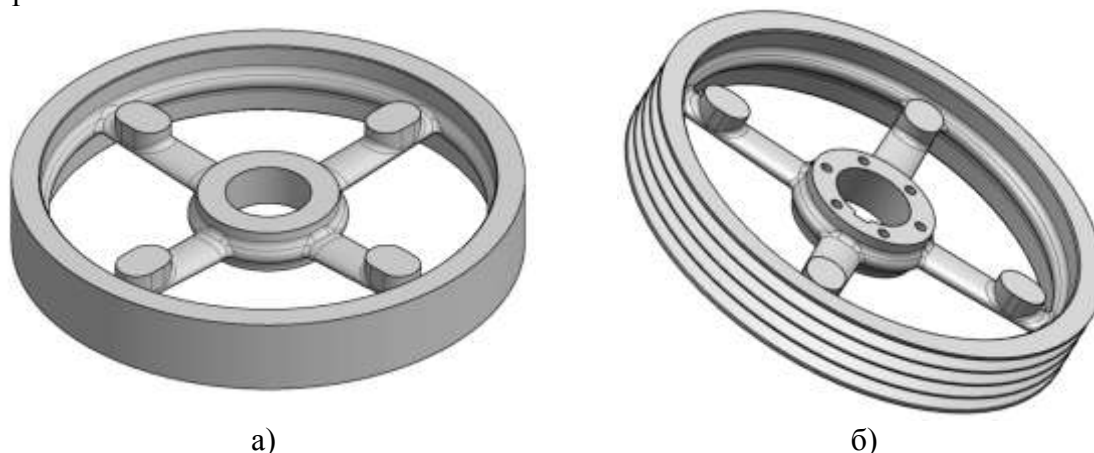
а) изготавливаемая отливка, б) конечная деталь «Шкив»
